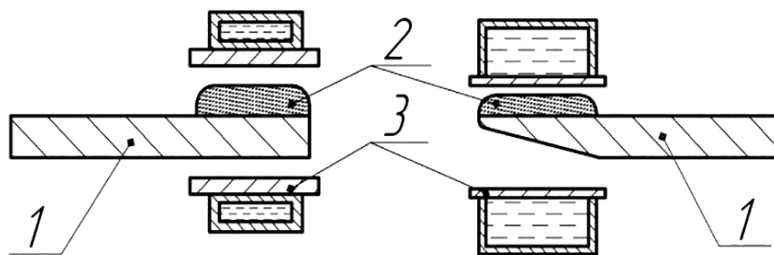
Схема наплавки деталей, имеющих в поперечном сечении форму пластины клина: 1 – деталь; 2 – шихта; 3 – индуктор
